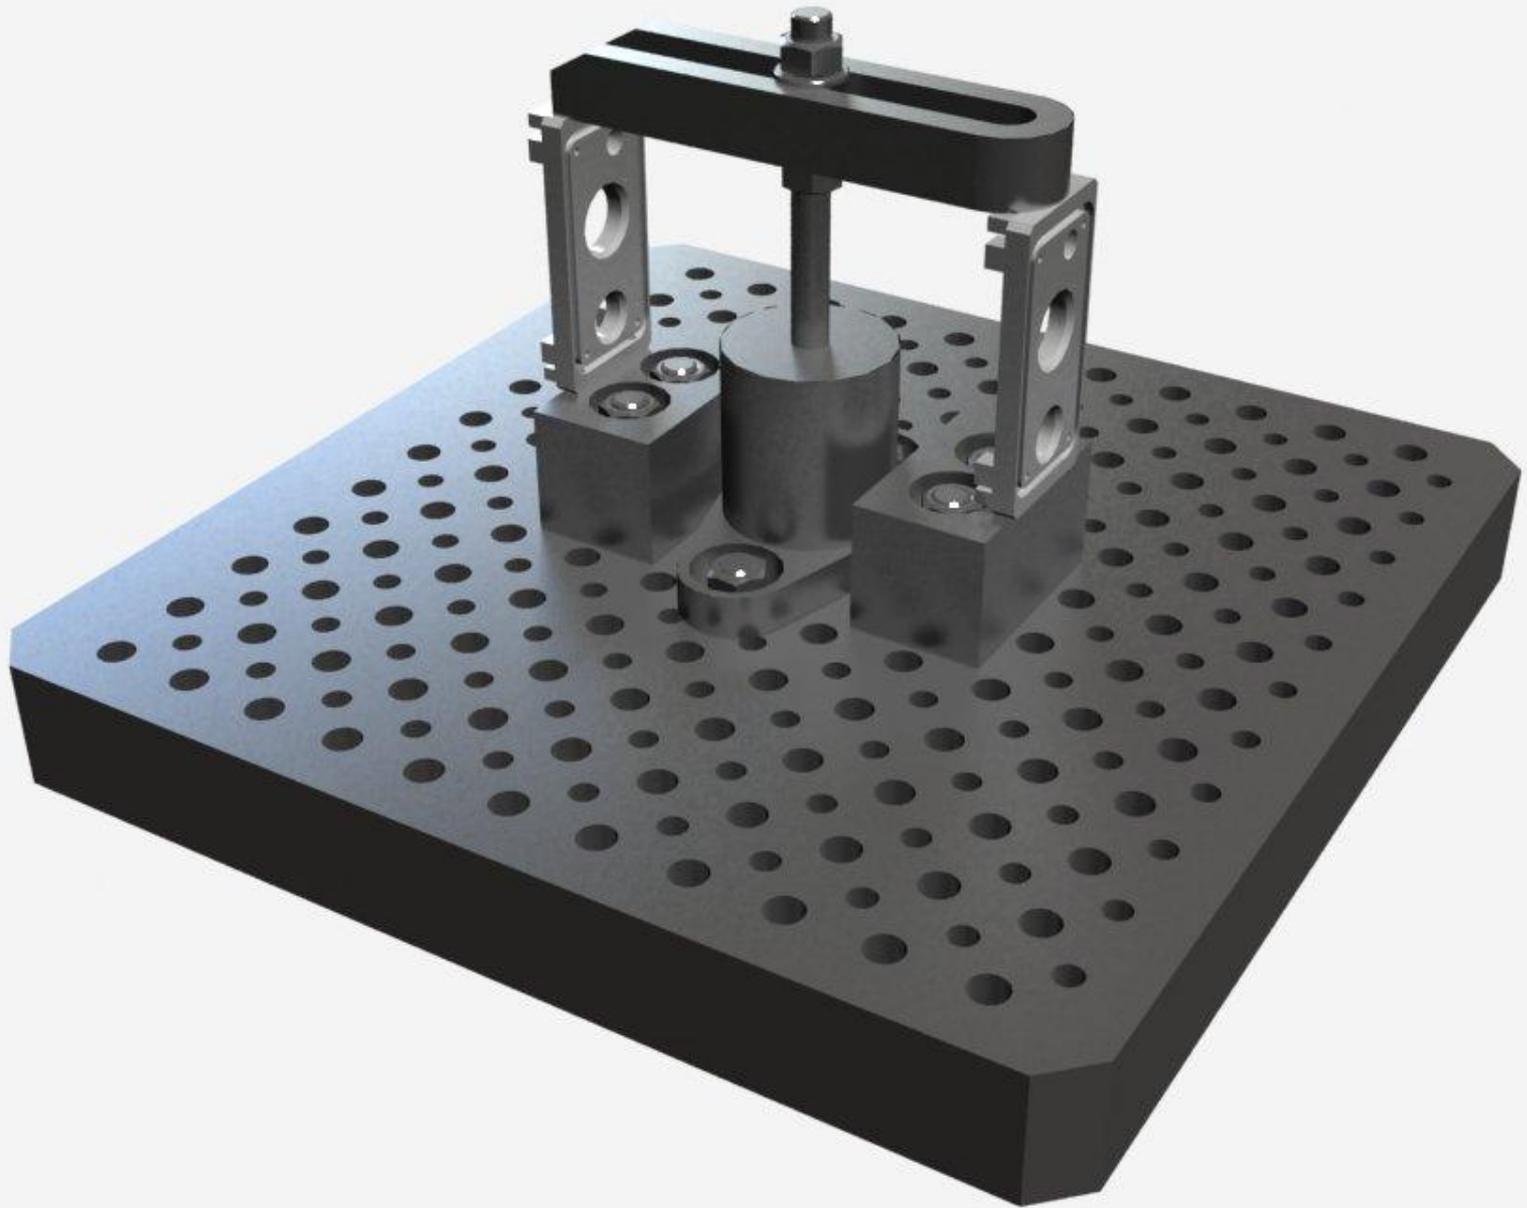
Базовый набор деталей и сборочных единиц универсально-сборных приспособлений:
